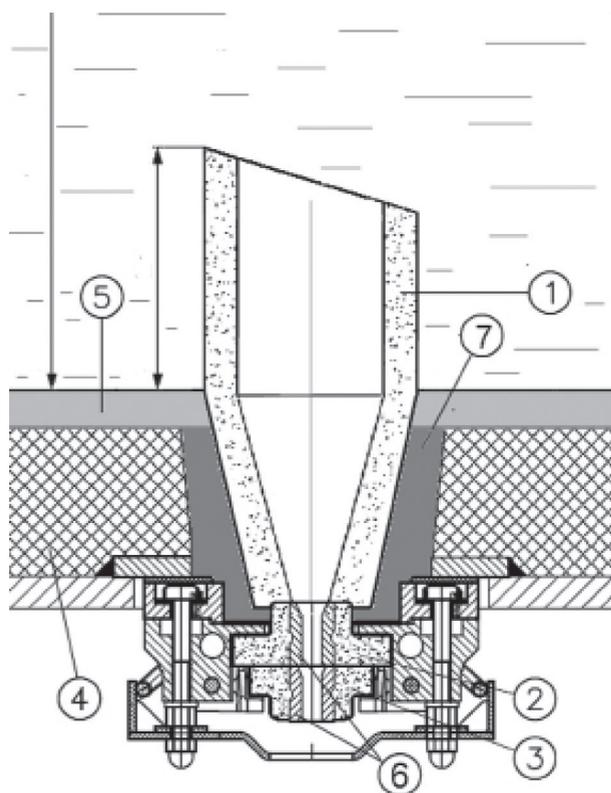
Разливочный узел промковша сорта МНЛЗ с системой быстрой замены стаканов-дозаторов CNC и стационарной воронкой: 1 – тационарная воронка; 2 – верхний стакан-дозатор усиленной конструкции; 7 – ремонтная масса; остальные обозначения совпадают с обозначениями на рис. 1
